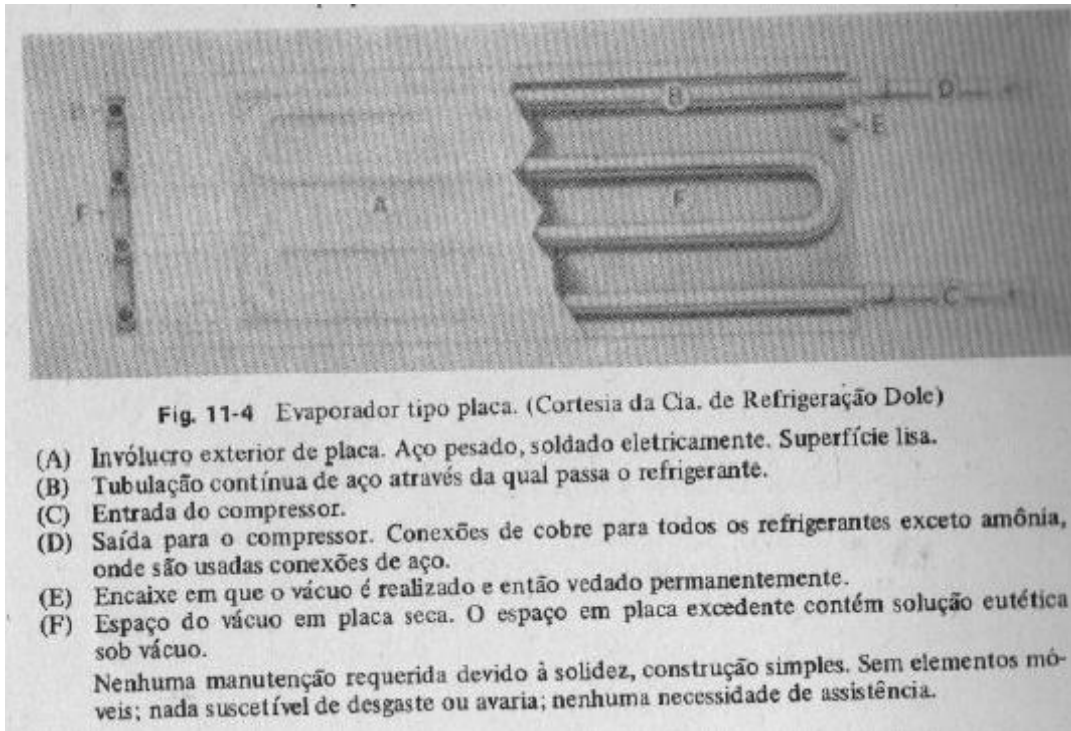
Evaporador de placa de tubulação instalada entre duas placas de metal soldadas [4].
